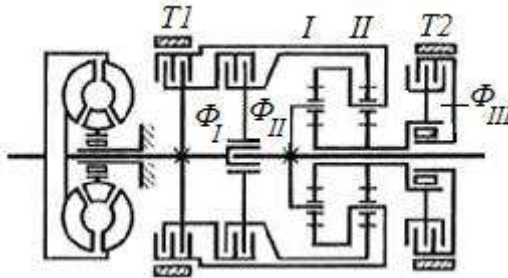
Гідромеханічна передача з планетарною коробкою передач
